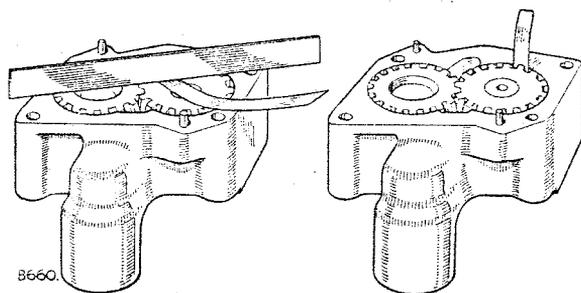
Comprobación de la tolerancia de los engranajes de la bomba.
